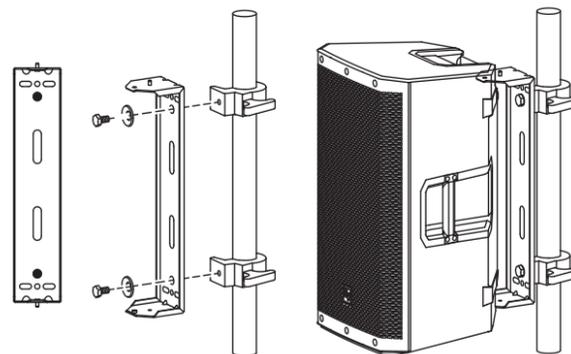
Montagem vertical usando braçadeiras de treliça TCA-1
